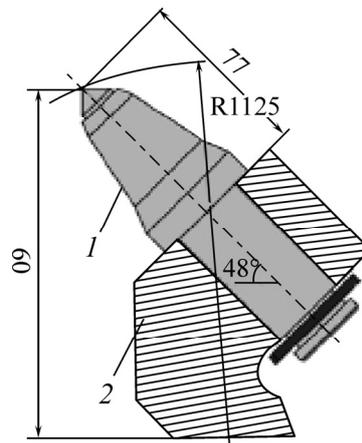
Тангенциальный поворотный резец для комбайна SL300: 1 — тангенциальный поворотный резец; 2 — резцедержатель
